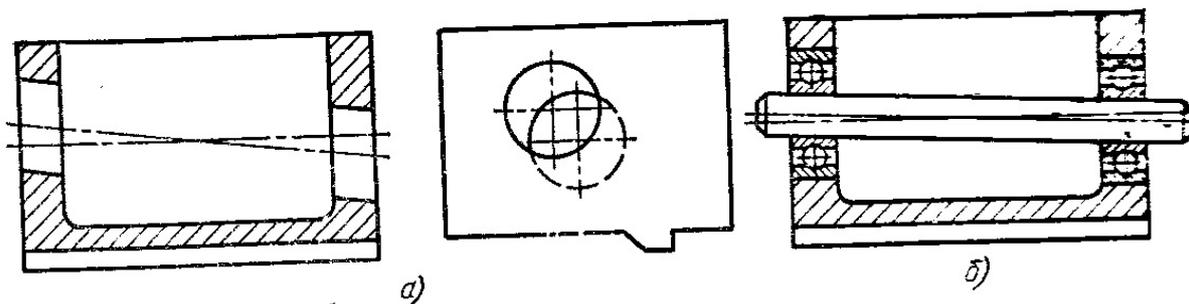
Поворот оси вращения вала относительно основных баз корпуса
